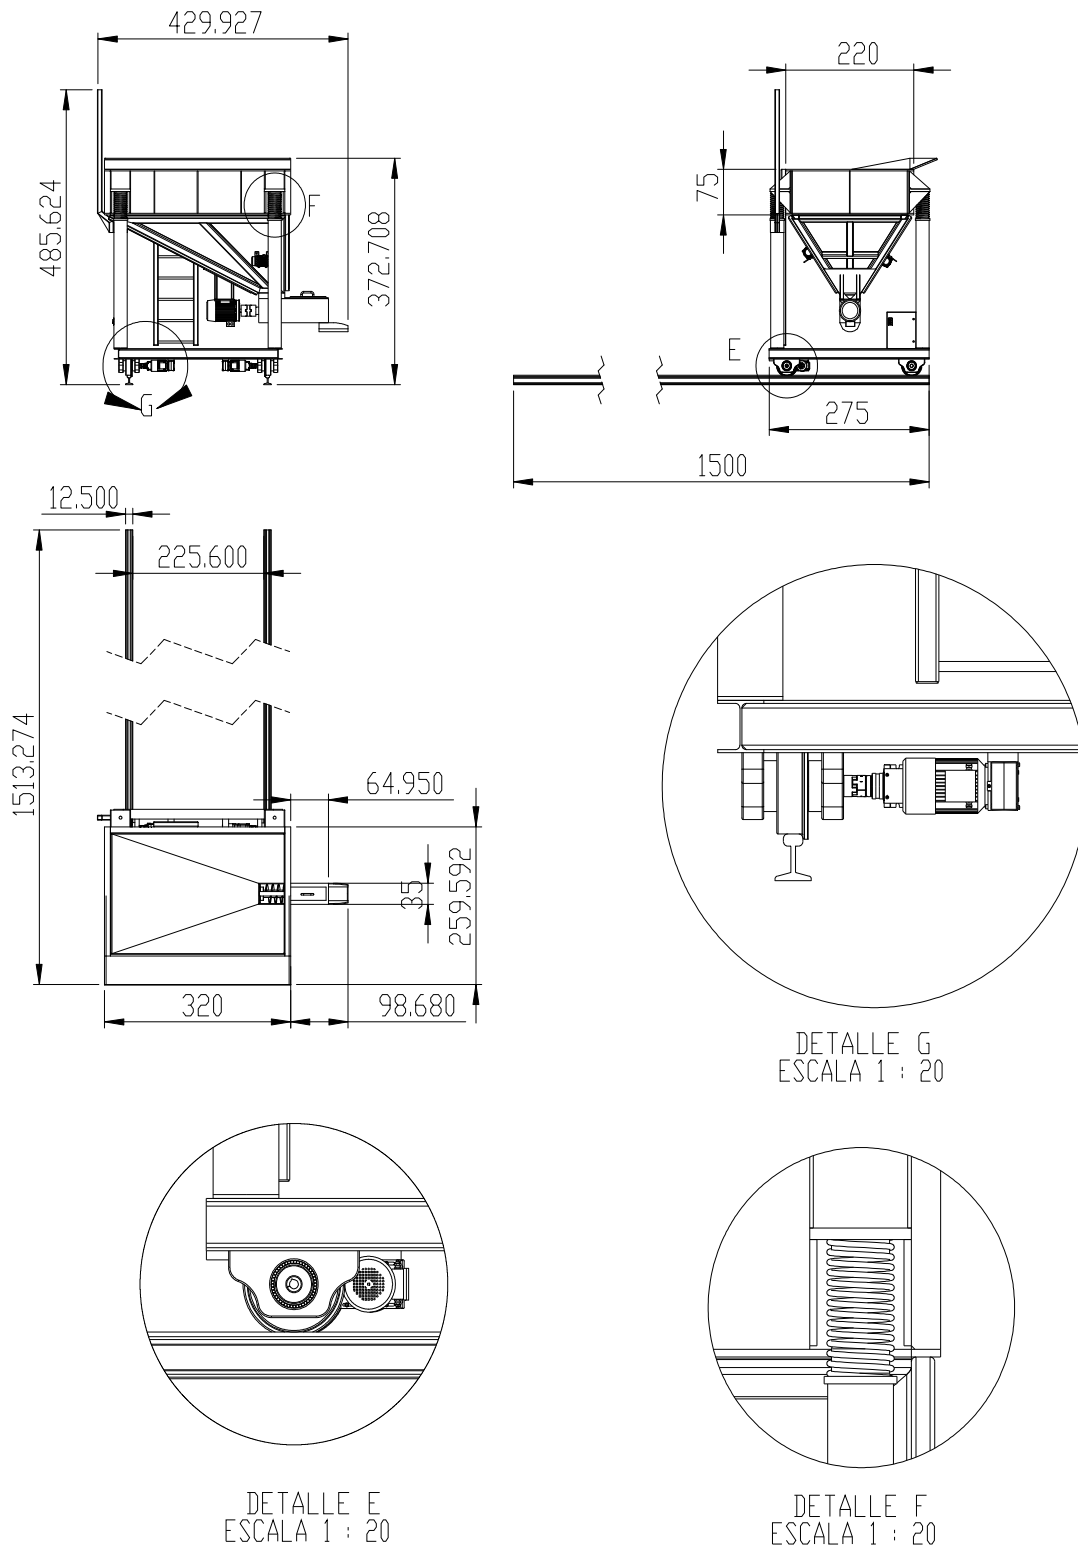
Despiece general de la unidad cargadora de material (detalle de ensamble).
